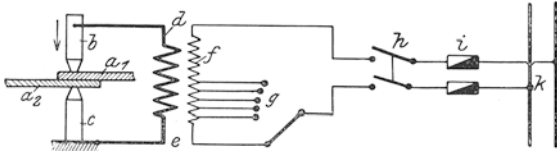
Schaltung und Stromzuführung bei Punktschweißmaschinen.
